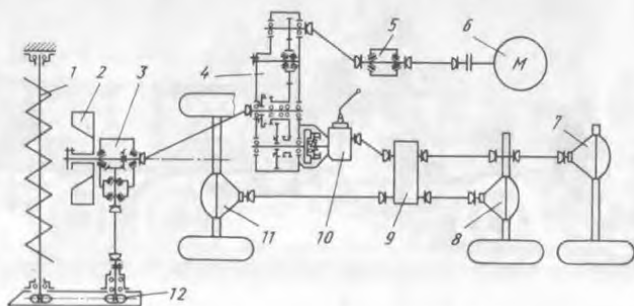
Кинематическая схема снегоочистителя ДЭ-204А
